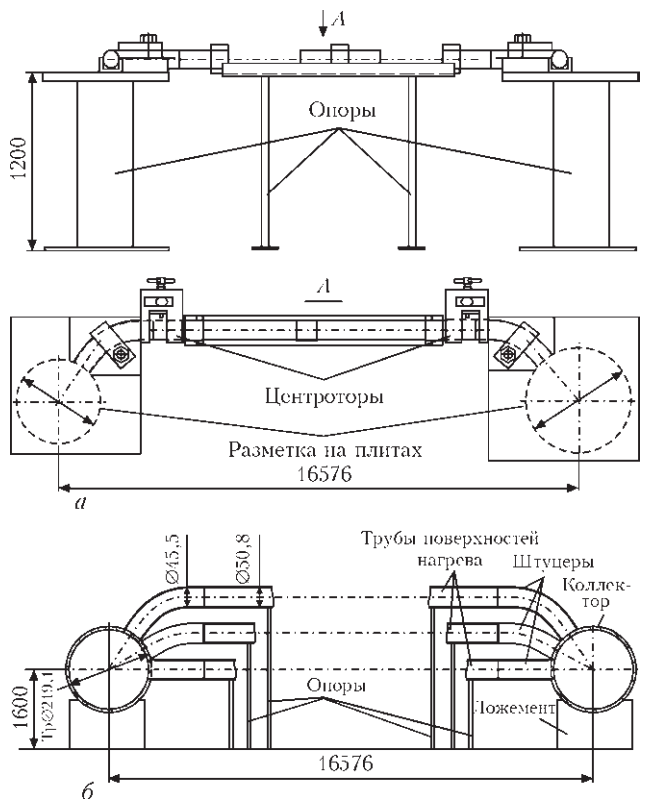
Стенды для сборки и сварки: а — стыковых соединений труб поверхности нагрева со штуцерами; б — угловых соединений коллектора с «трубной плетью»
